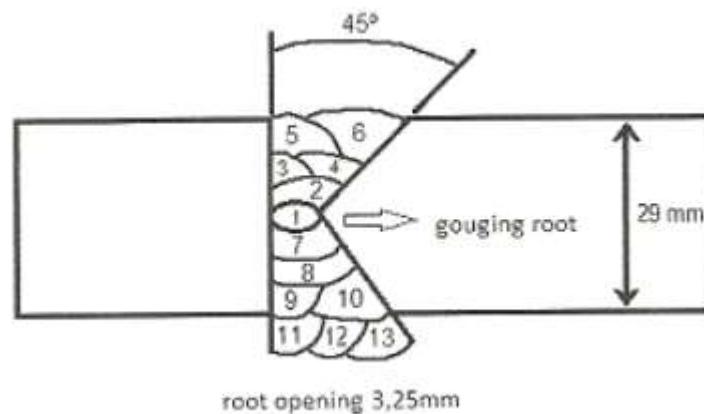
Detalhamento da junta soldada referente a EPS-006. Fonte: autor
